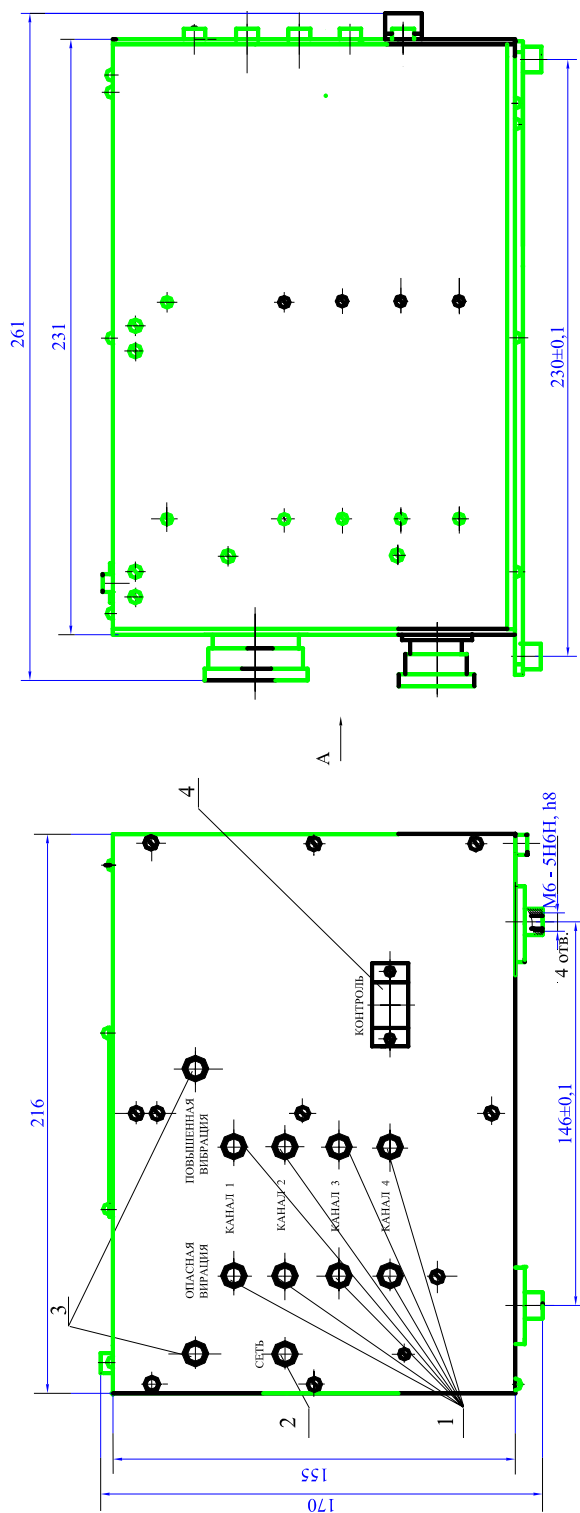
(1 из 2) - Габаритно - установочные размеры блока БЭ-38-25-1
